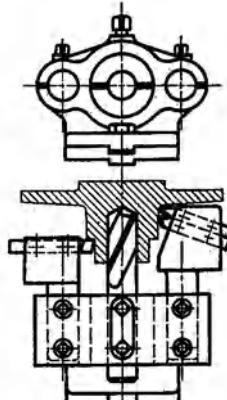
Halter für Bohr- und Drehwerkzeuge auf dem Revolverschlitten.
